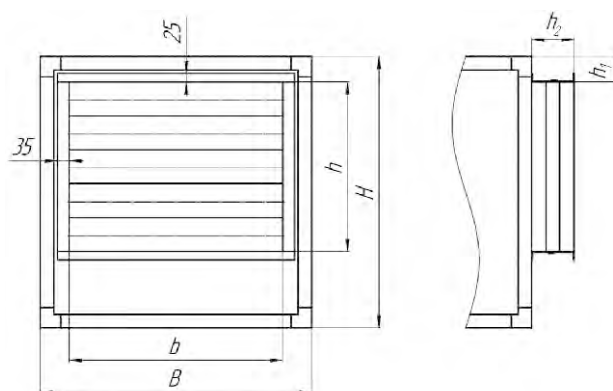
Габаритные и присоединительные размеры. Передняя панель с клапаном.
